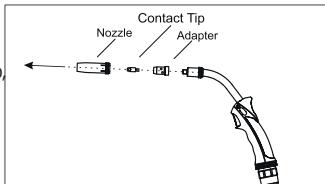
Remover O Bico, A Peça De Contacto E O Adaptador
